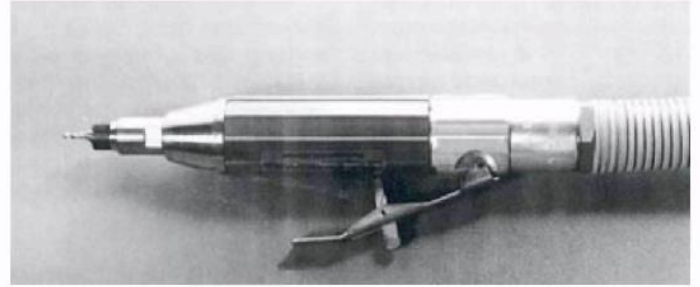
Шпиндель для фрезерования с пневмоприводом
